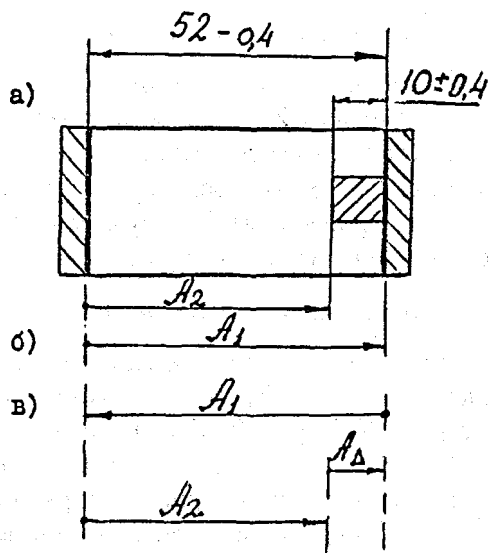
Эскиз валика (а); размерная схема его обработки (б);
